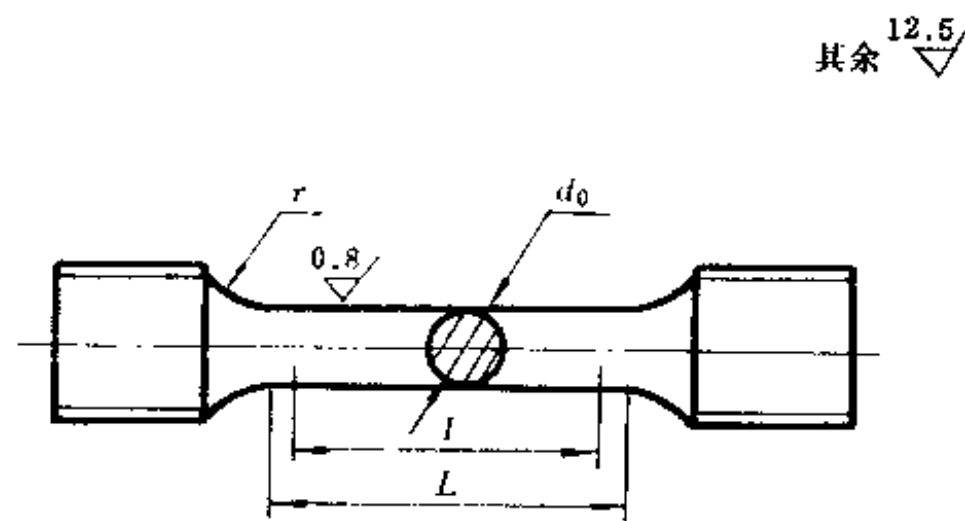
焊缝及熔敷金属拉伸试样(三)
